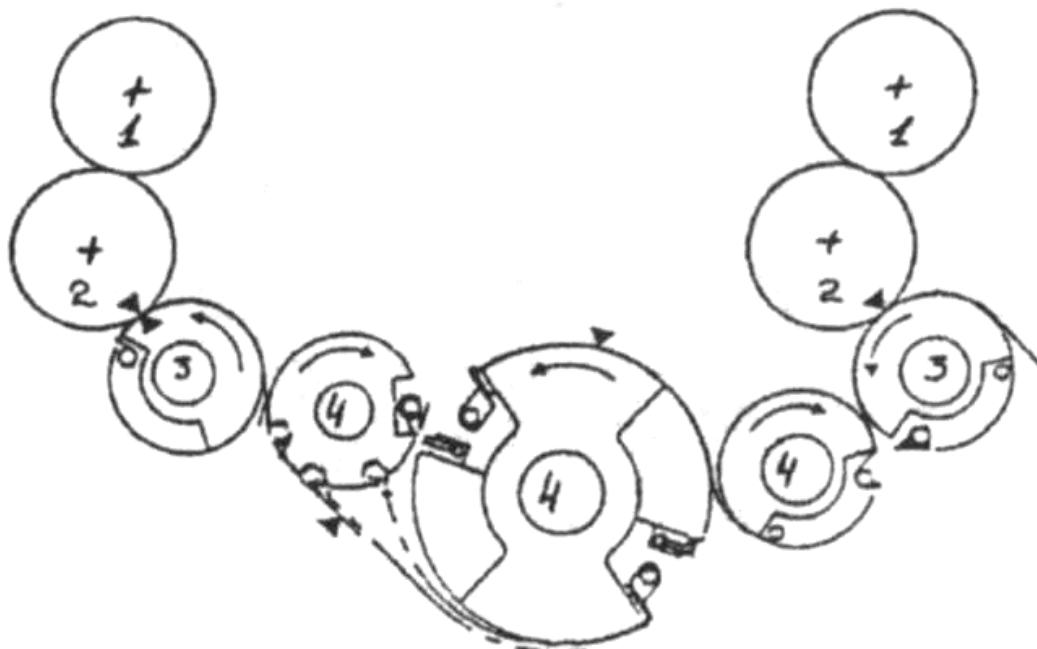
Схема печатного аппарата: 1 — формные цилинды; 2 — офсетные цилинды; 3 — печатные цилинды; 4 — передаточные цилинды
